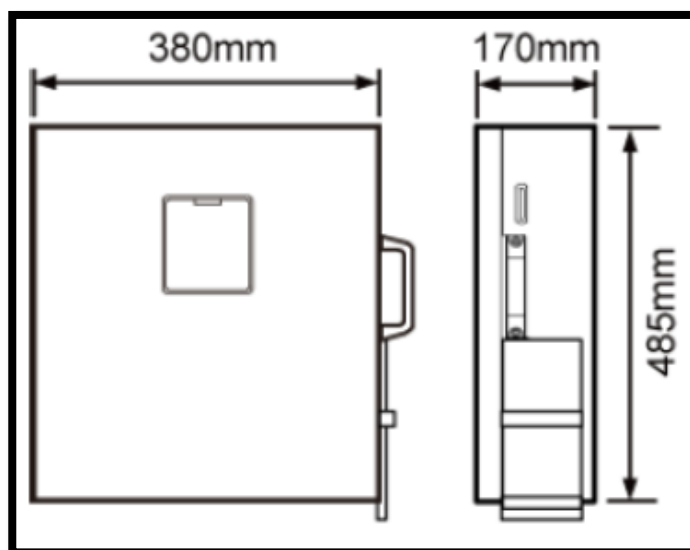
Dimensiones de la RRU, peso 25 Kg
